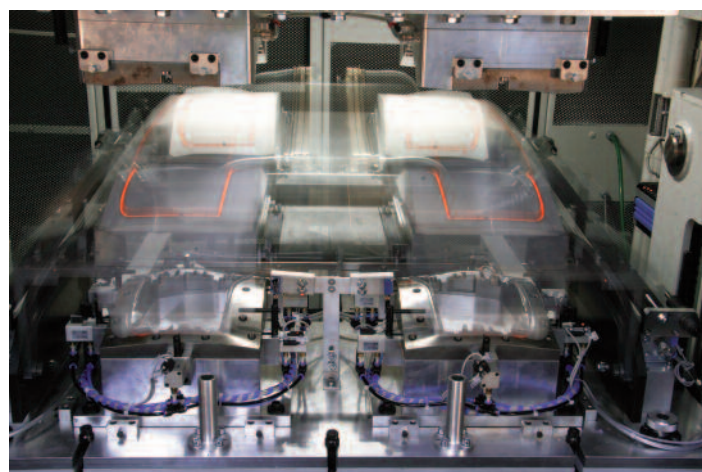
Clean Vibration Technology (CVT): Umstellphase beim kombinierten Schweißen einer automobilen Rückleuchte
